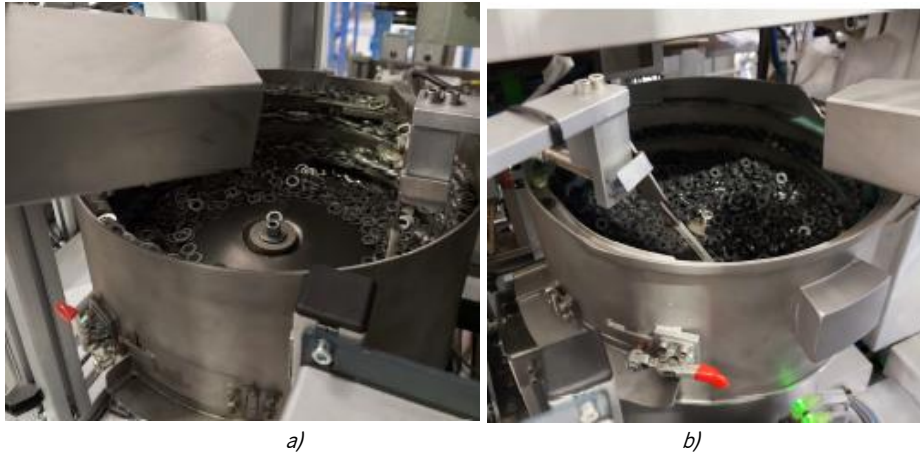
a) Alimentador de anilhas; b) Alimentador do shaft seal
